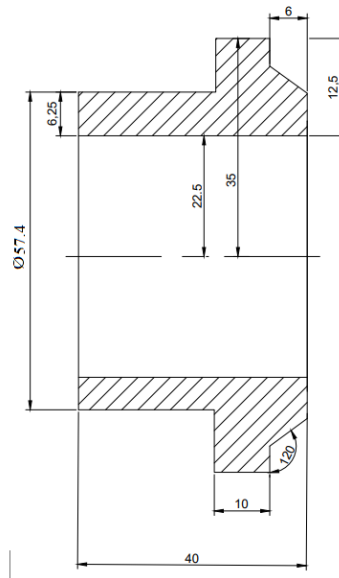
Готова втулка для притискання фільтру дорна
